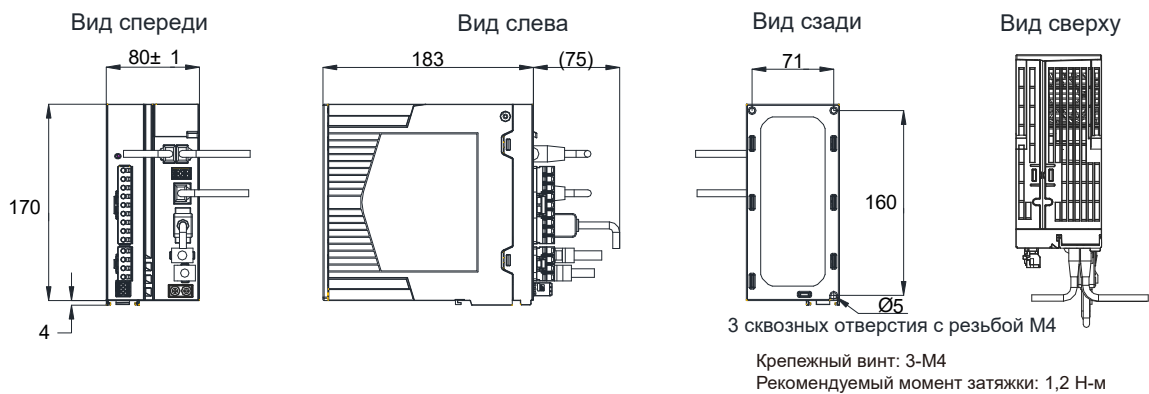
Габаритные размеры для типоразмера D (ед. изм: мм)
